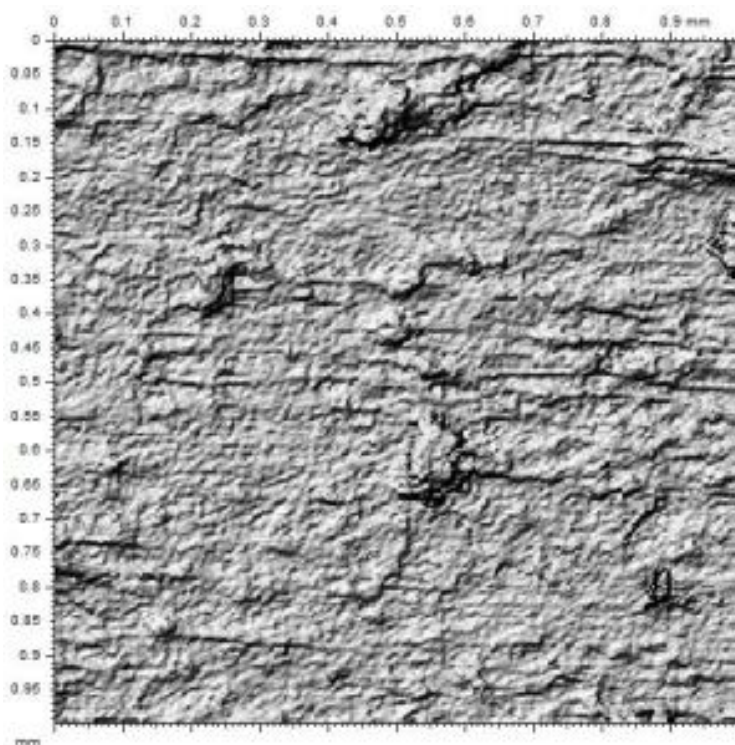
2D zobrazení broušeného povrchu oceli 19 436
